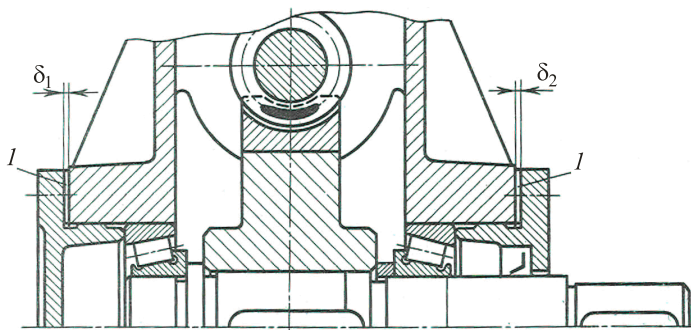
Регулирование осевого положения вала червячного колеса
